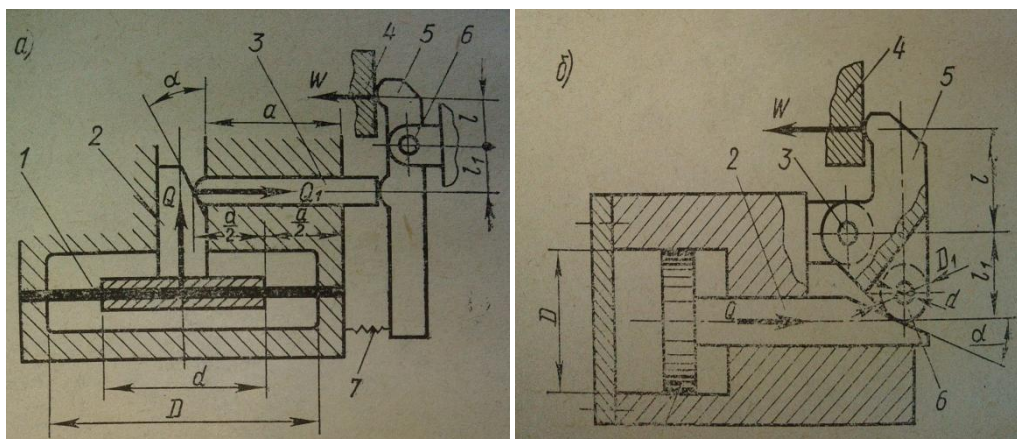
Схема затискних пристроїв з пневмоприводом
